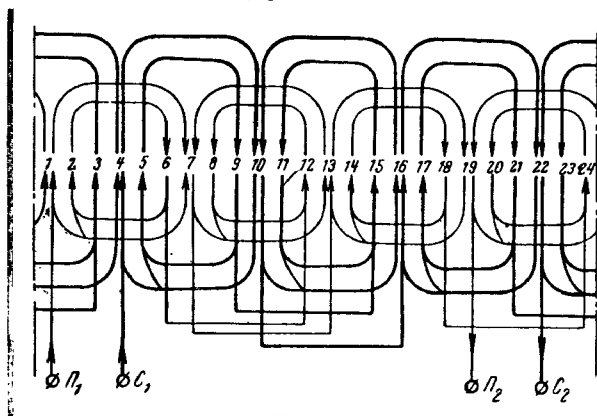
Схема однослойной катушечной (коцентрической) обмотки «вразвалку» однофазного конденсаторного двигателя.
